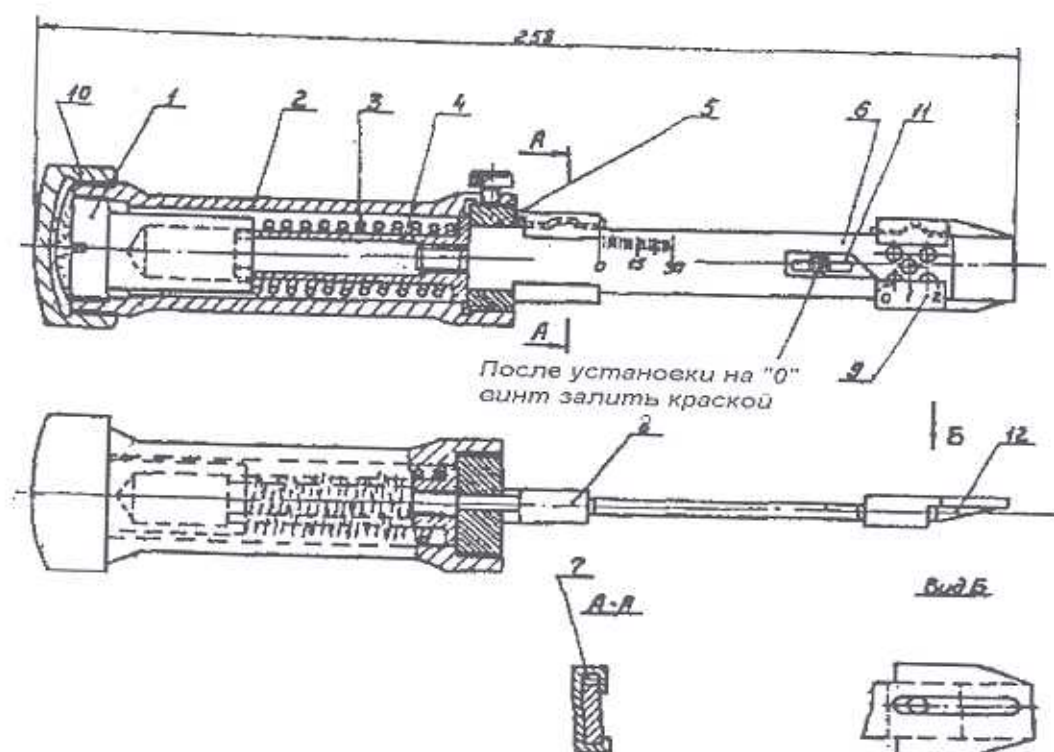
Специальный щуп для контроля запрессовки сердечника статора:
